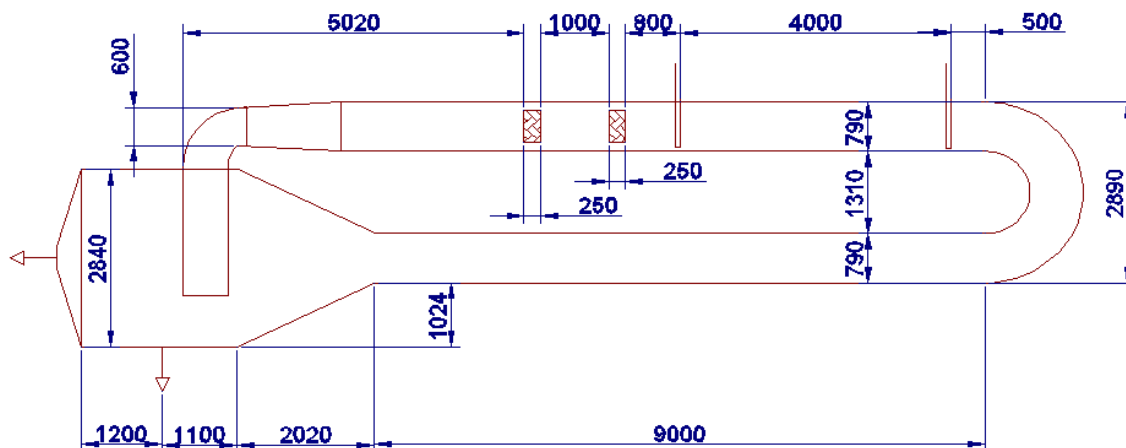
Bemaßung des Reaktors in mm (Reaktor hier liegend gezeichnet; links ist oben)
